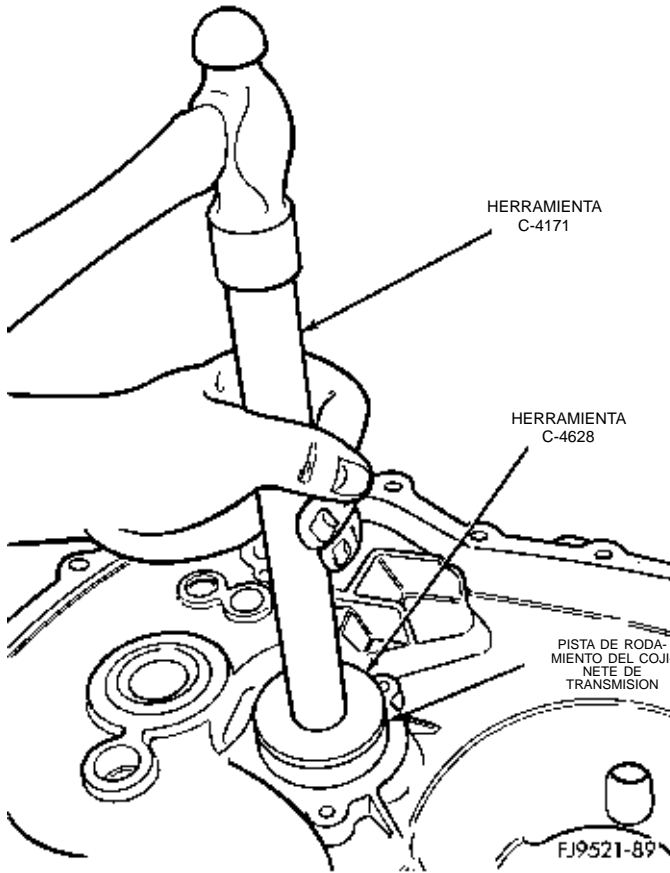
Desmontaje de la pista de rodamiento del cojinete de transmisión
